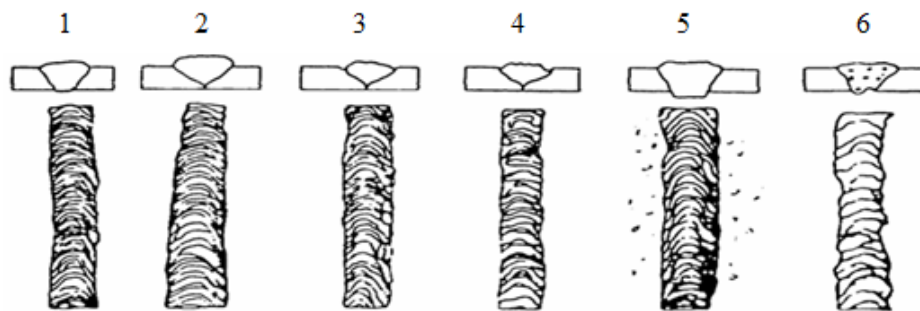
Aspectos Superficiales en la Soldadura.
